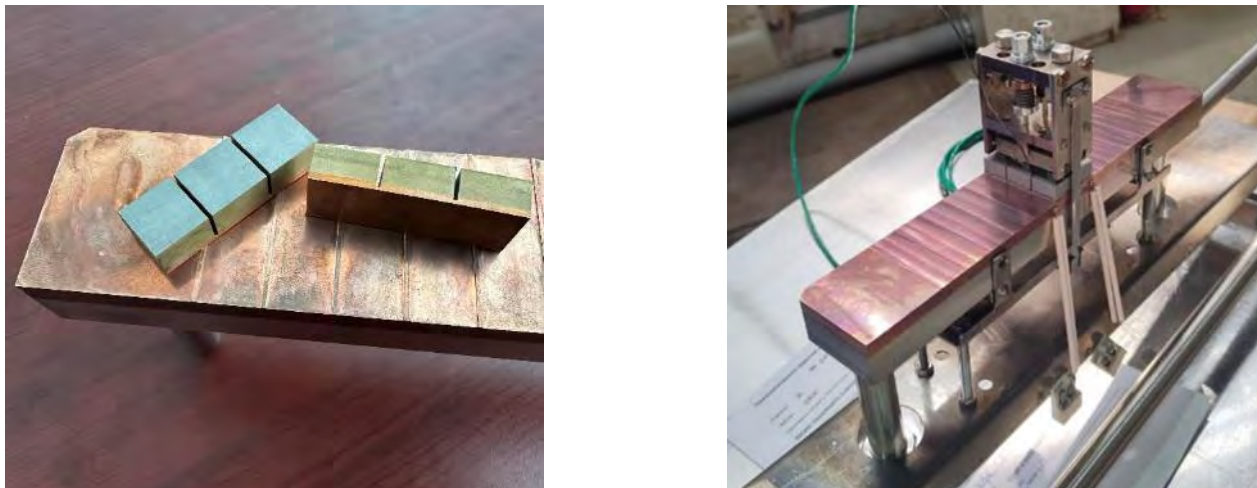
Подготовка к пайке макета с W/Cu-плитками
